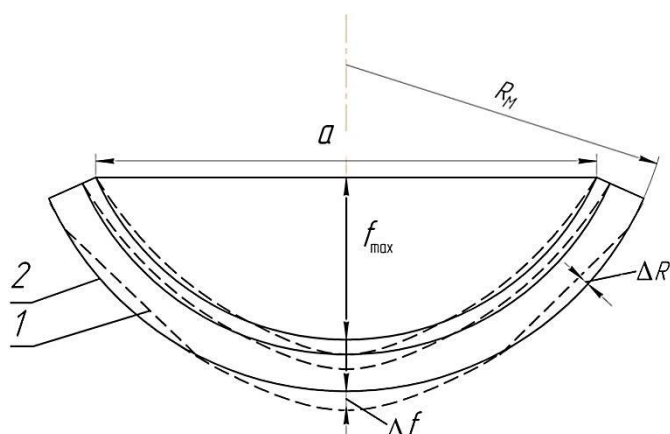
Схема оценки качества штамповки сваренного биметалла:
